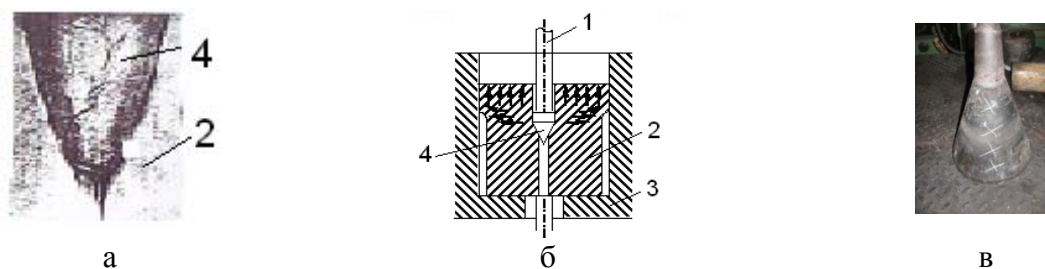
Схема прошивки трубной заготовки (а) и экспандирования гильзы (б) и характерная картина износа экспандера (в) прошивного пресса 12 МН трубопрессовой линии фирмы SMS MEER: 1 – стержень оправки; 2 – трубная заготовка; 3 – контейнер; 4 – оправка или экспандер
